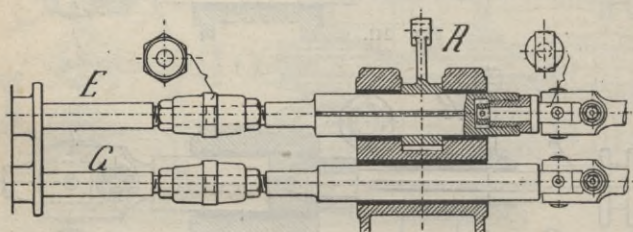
1251. Die Muttern mit Rechts- und Linksgewinde gestatten ein bequemes Einstellen der Schieber selbst während des Ganges der Maschine.
